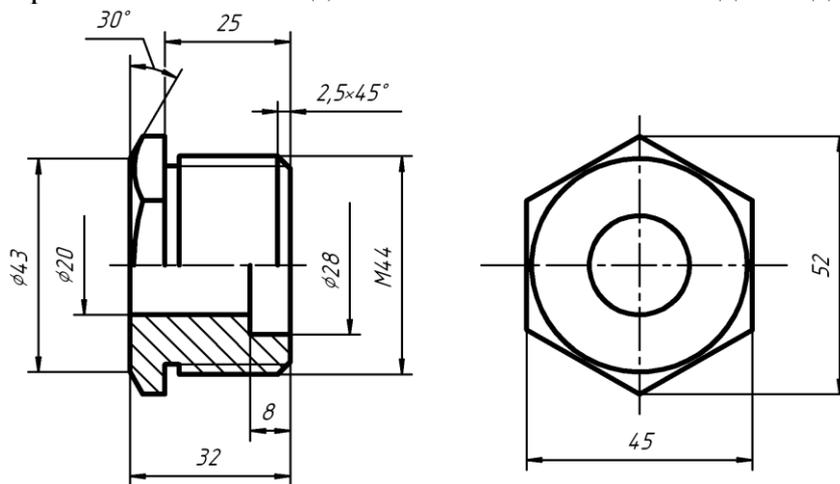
Чертеж детали, имеющей шестигранный элемент
